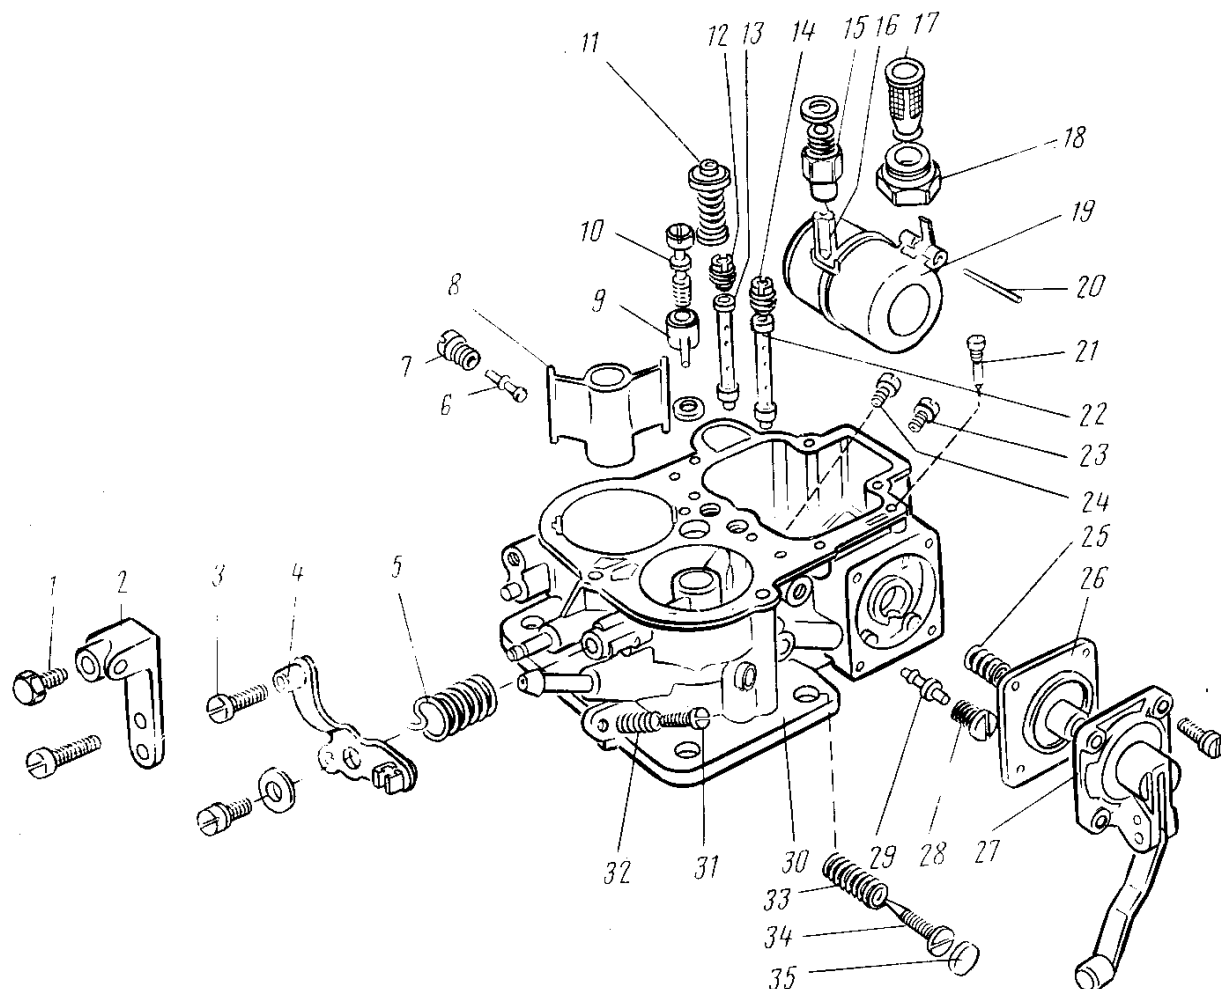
Детали корпуса карбюратора ДААЗ-2101-20: 1 — винт крепления оболочки троса; 2 — кронштейн; 3 — винт крепления троса; 4 — рычаг привода воздушной заслонки; 5, 25, 32 — пружины; 6 — топливный жиклер переходной системы вторичной камеры; 7 — корпус жиклера; 8 — малый диффузор; 9 — распылитель насоса-ускорителя; 10 — клапан-винт насоса-ускорителя; 11 — клапан; 12 — главный воздушный жиклер вторичной камеры; 13, 22 — эмульсионные трубки вторичной и первичной камер; 14 — главный воздушный жиклер первичной камеры; 15 — седло игольчатого клапана; 16 — игольчатый клапан; 17 — фильтр; 18 — пробка; 19 — поплавок; 20 — ось; 21 — регулировочный винт насоса-ускорителя; 23 — главный топливный
